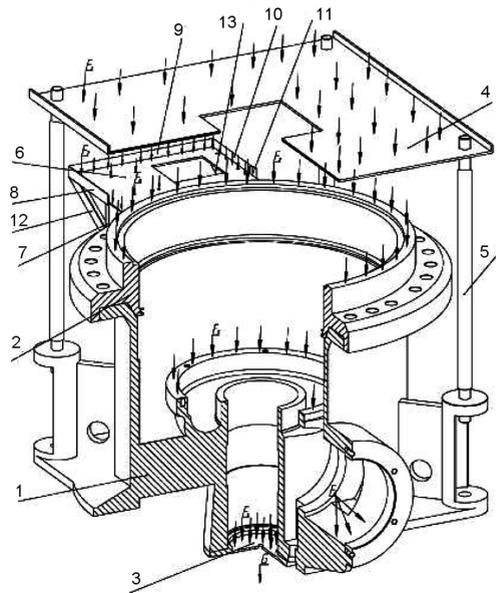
Расчетная схема конусной дробилки КСД-900: 1 — станина; 2 — кольцо опорное; 3 — крышка подпятника; 4 — площадка; 5 — стойка; 6 — плита опорная; 7 — уголок 1; 8 — уголок 2; 9 — уголок 3; 10 — уголок 4; 11 — уголок 5; 12 — уголок 6; 13 — уголок 7
